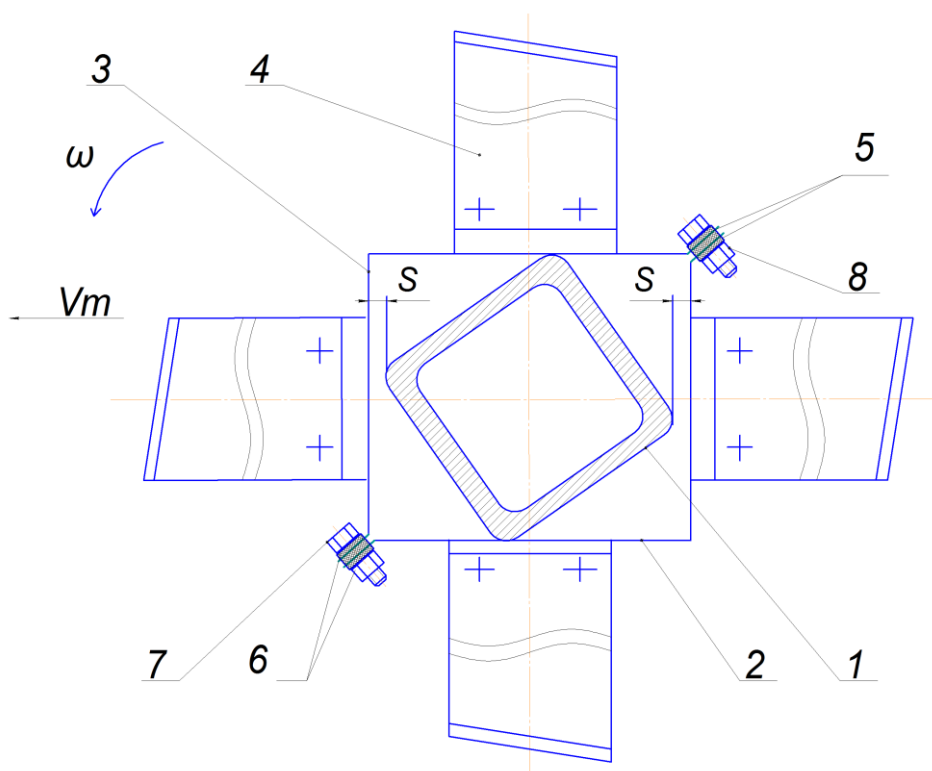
Конструкция № 2 предохранительного устройства для секции почвообрабатывающей фрезы
